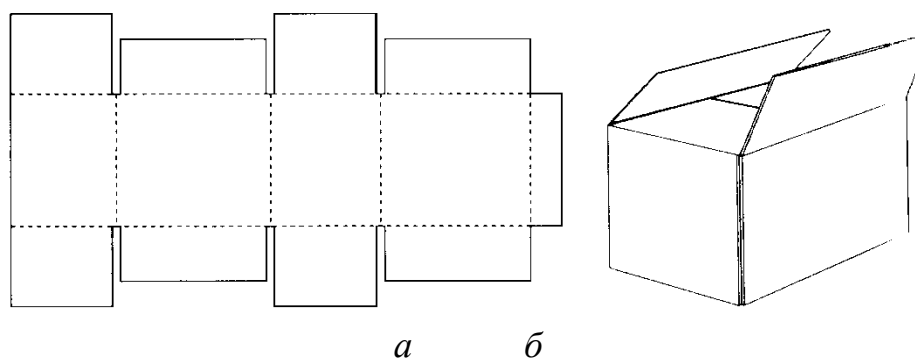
Развертка (а) и внешний вид (б) ящика с четырьмя клапанами
